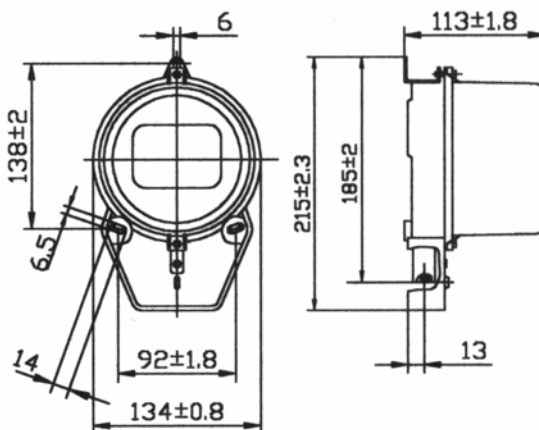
Габаритные и установочные размеры счетчика СО-ЭЭ6706
